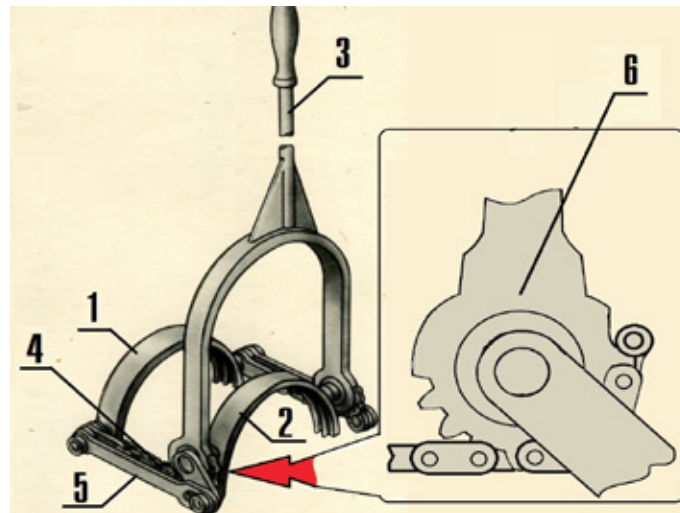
Монтажный (цепной) ключ: 1 — передний захват, 2 — задний захват, 3 — рычаг, 4 — цепь, 5 — тяга, 6 — блок
